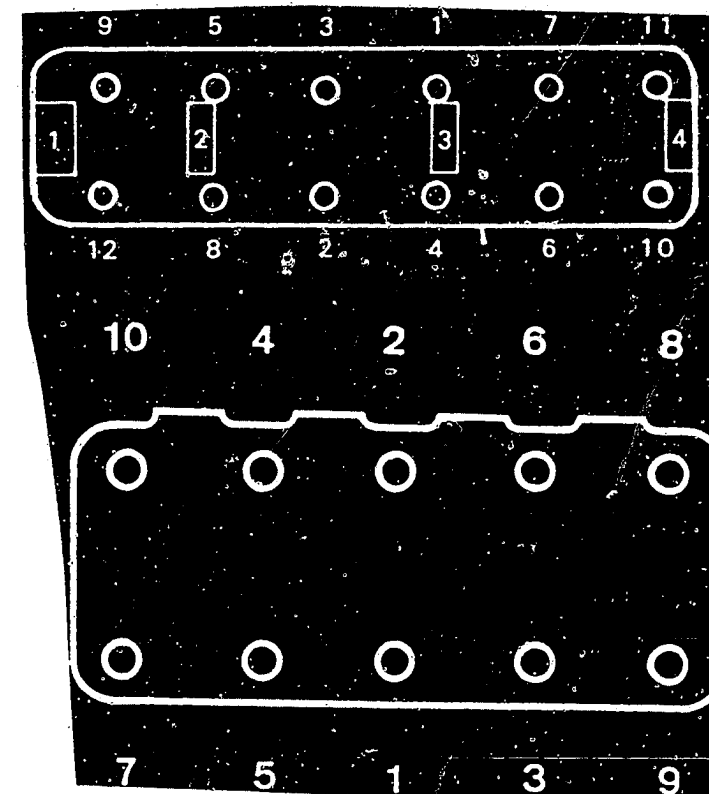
Richtige Reihenfolge für das Festziehen der Zylinderkopfschrauben (oben 4-Zylinder-, unten 6-Zylindermotor) in drei Stufen mit 40/60Nm plus einem Drehwinkel von 180°.
